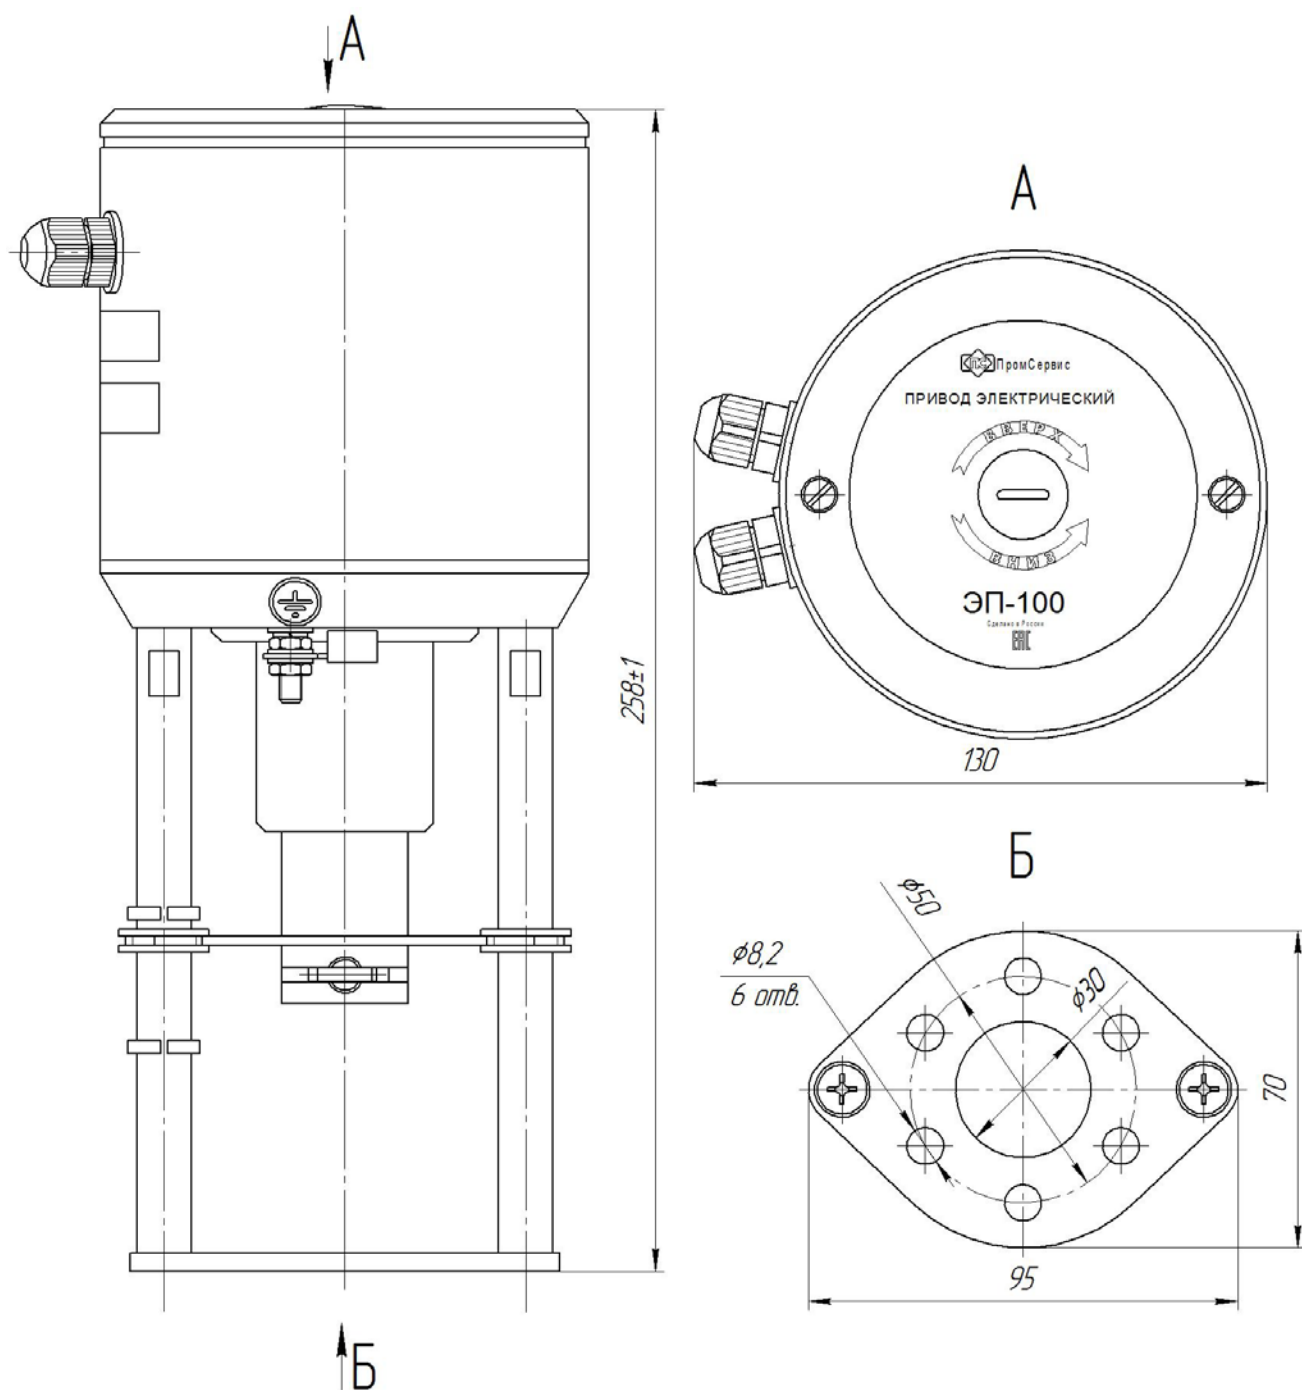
Габаритные и присоединительные размеры привода исполнения ЭП-100-02
